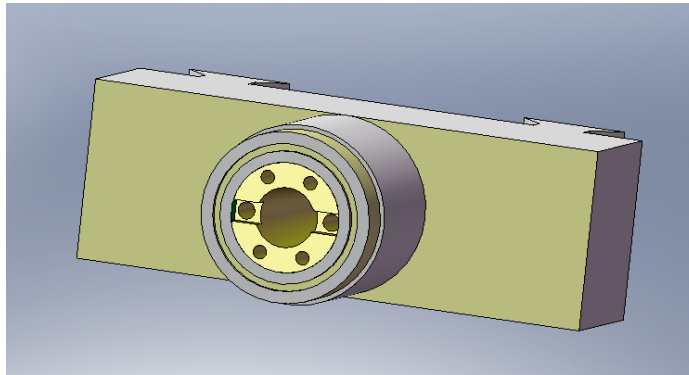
Зміна шпинделя IP500 ПМФ4-09
